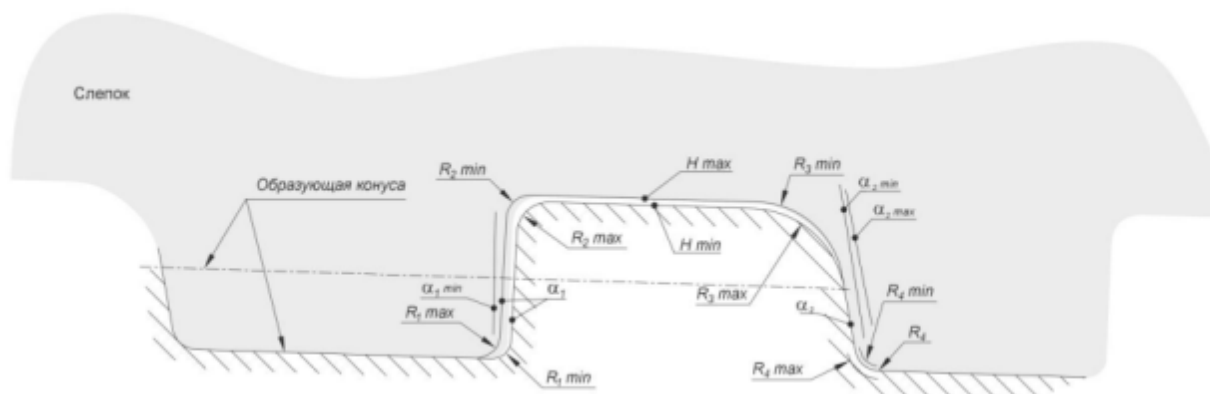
Контроль профиля резьбы трубы по слепкам
